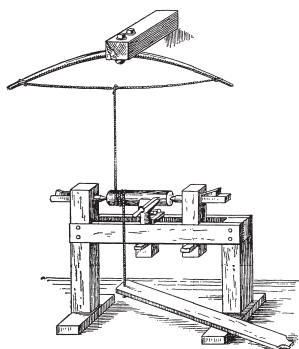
Лучковый педальный токарный станок с опорной площадкой для резца
